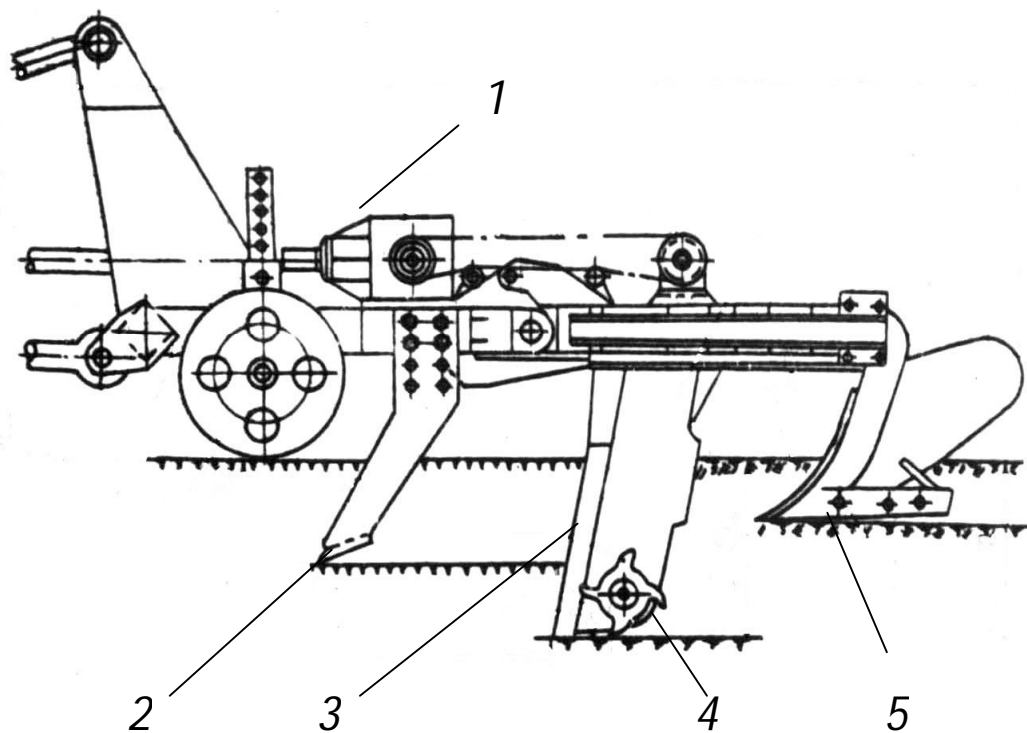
Устройство для мелиоративной внутрипочвенной фрезерной обработки почвы ПМС-70, вид сбоку.
